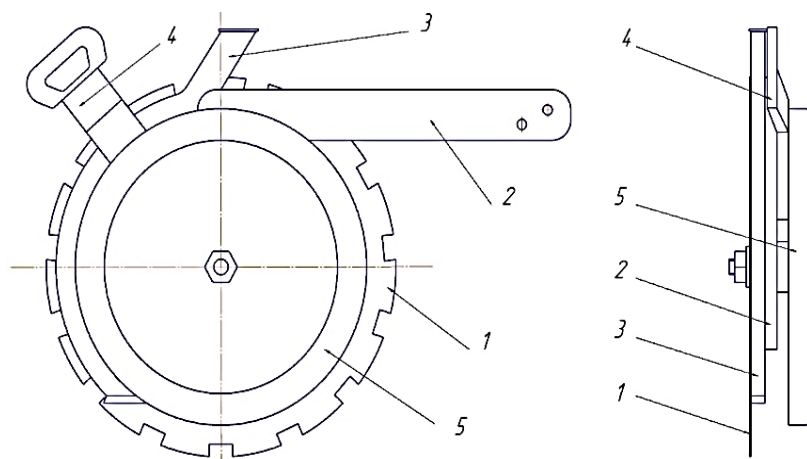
Однодисковый сошник с нулевым углом атаки и полиуретановой регулируемой ребордой: 1 – диск; 2 – корпус; 3 – семянаправитель; 4 – регулятор глубины; 5 – опорный каток
